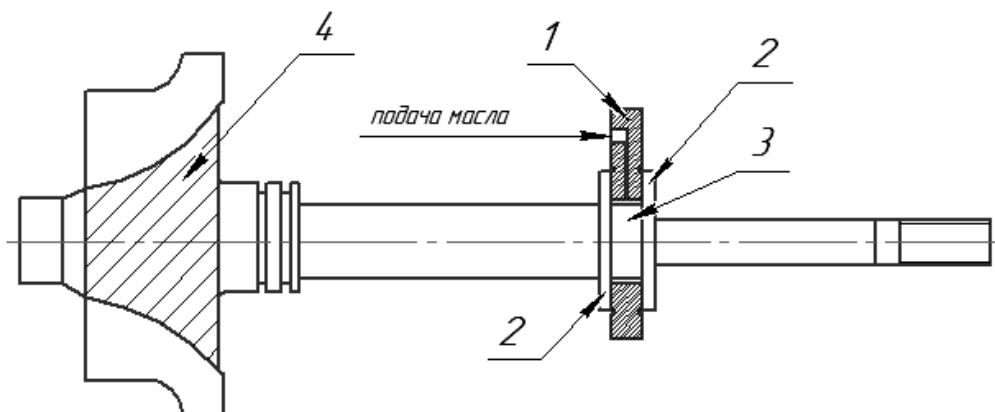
Схема сборки пары трения ротор-упорный подшипник турбокомпрессора
